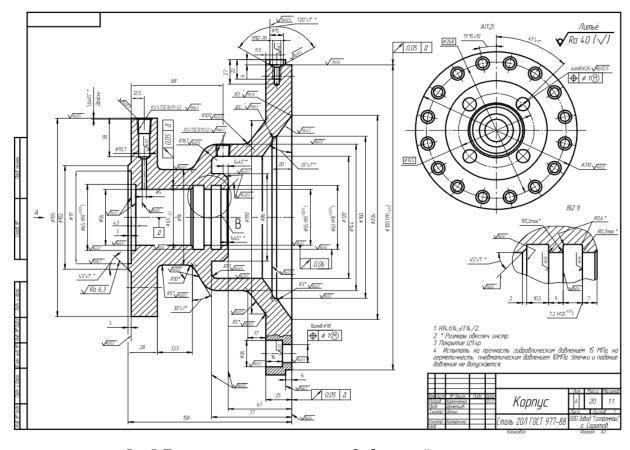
Пример конструкторского чертежа обрабатываемой детали: корпус
